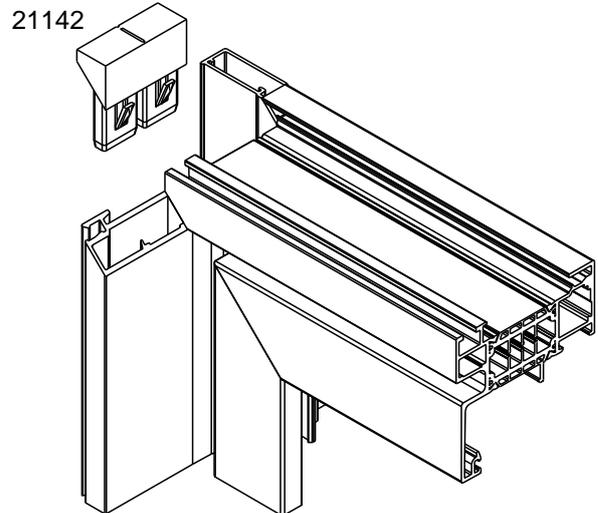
DETAILS D'ASSEMBLAGE DORMANT EN PARTIE HAUTE - Passage VR
